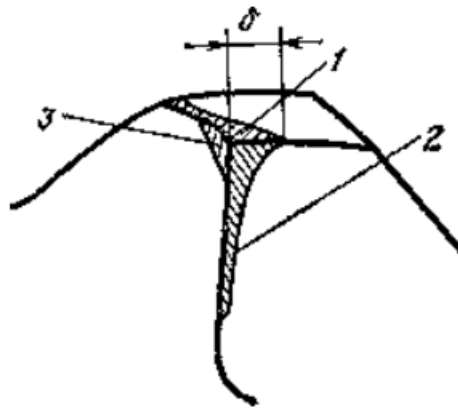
Знос зуба черв'ячної фрези:
